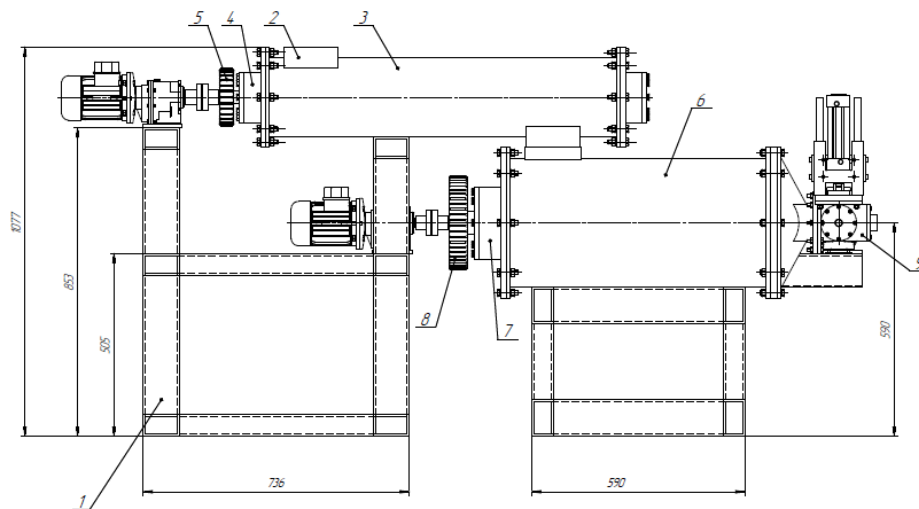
Загальний вигляд змішувальнобродильноформуального агрегату: 1- станина; 2 – камера попереднього змішування, 3 – змішувальна камера основного змішування; 4 – підшипниковий вузол; 5 – зубчаста передача приводу змішувальної частини; 6 – камера бродіння; 7 - підшипниковий вузол валу камери бродіння; 8 – зубчаста передача приводу камери бродіння; 9 – формувальний вузол.
